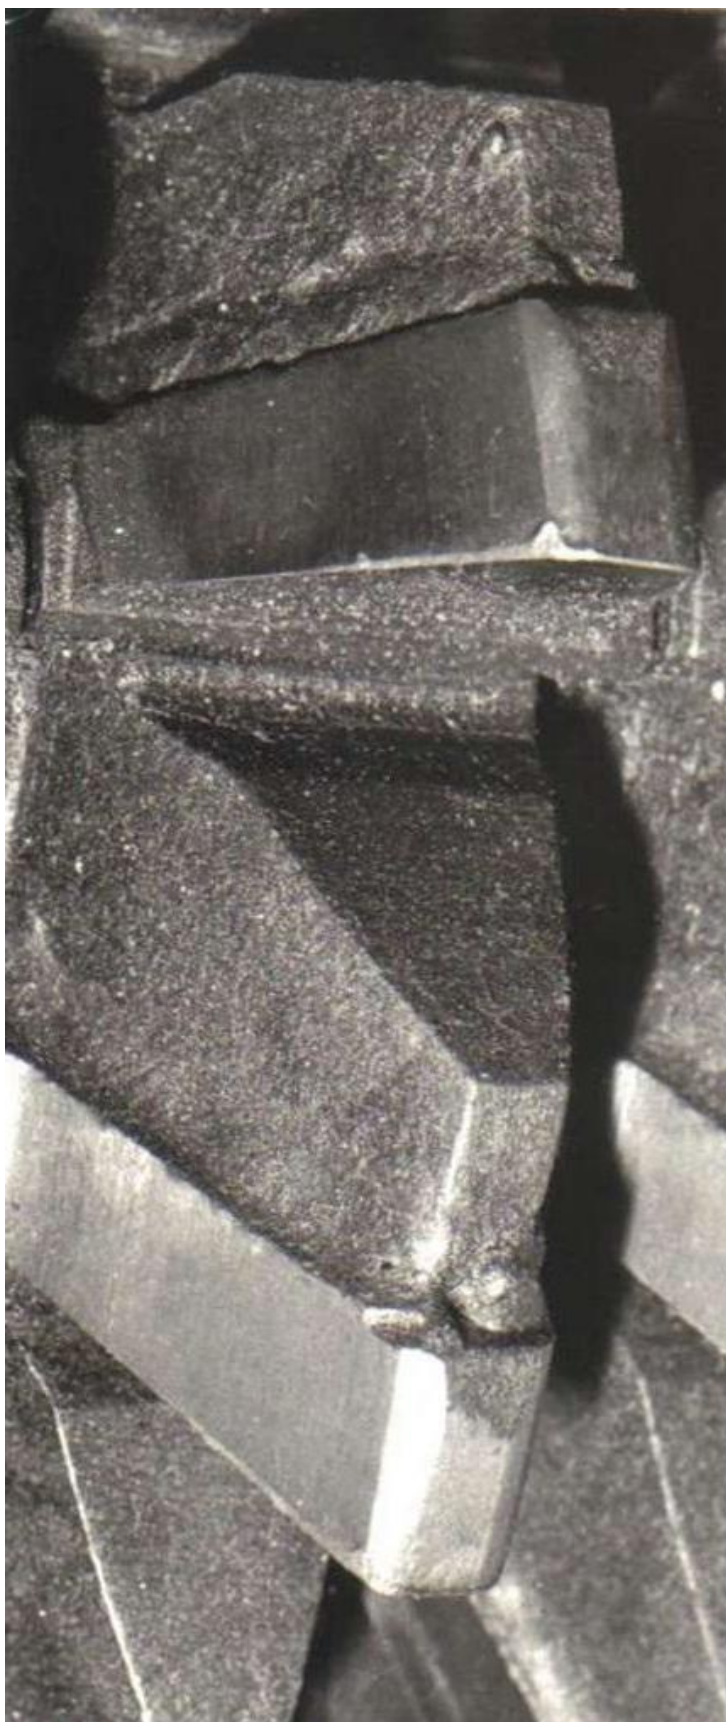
Підвищений знос зубів чистової швидкорізальної фрези збірно-звареної конструкції
